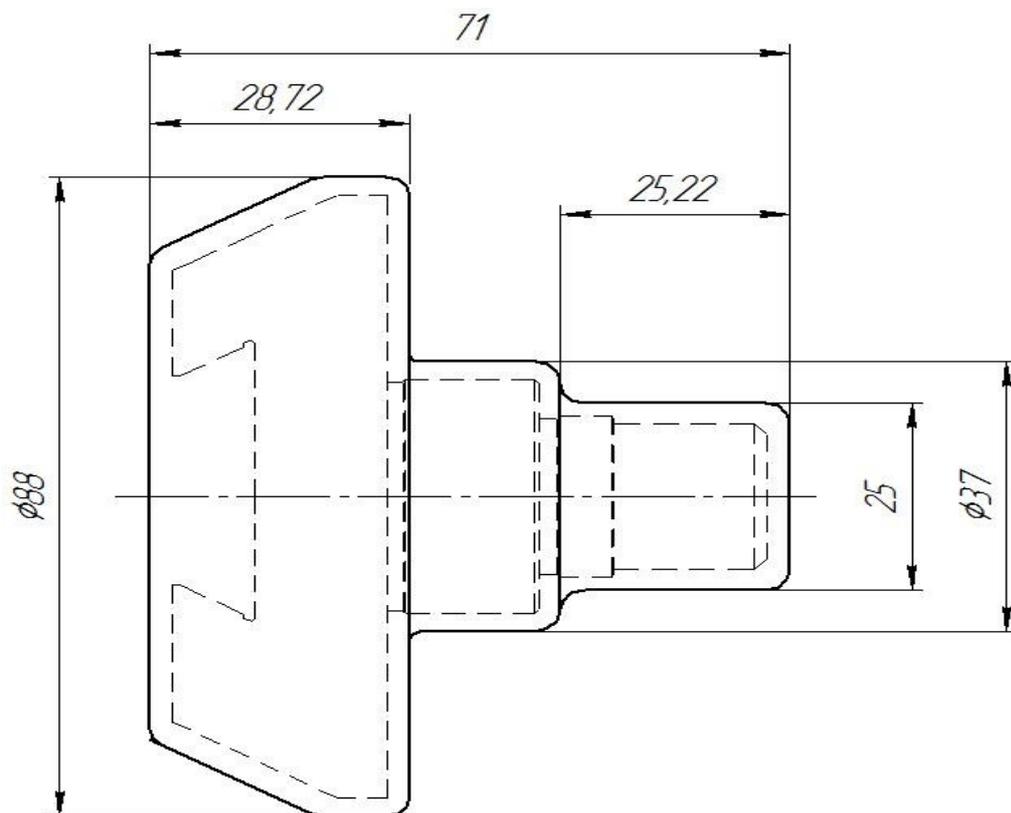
Эскиз заготовки полученной метод литья в металлических формах.
